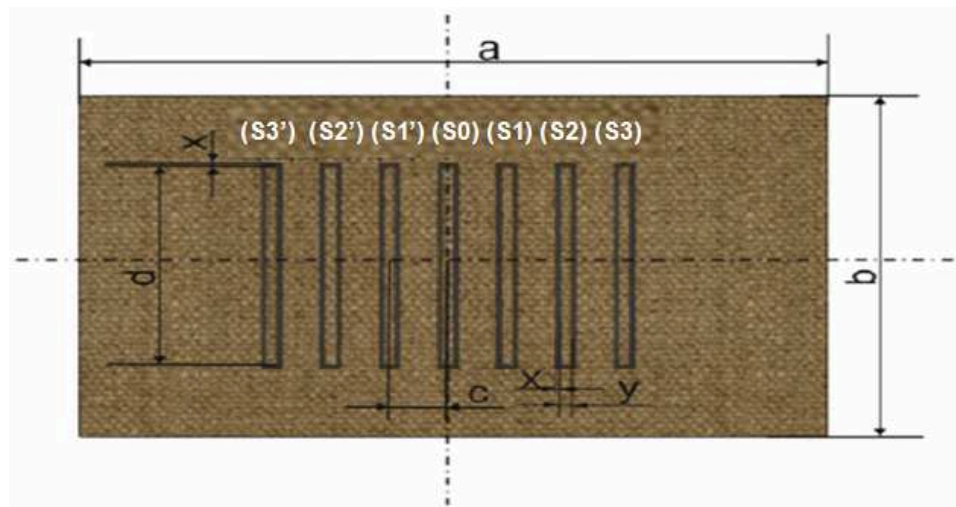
Dimensions géométriques de la plaque PCB munie de sondes intégrées sur sa surface :
